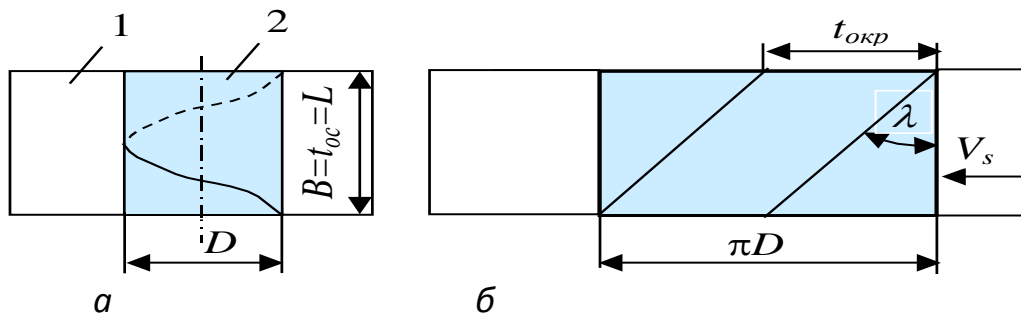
Резание фрезой с винтовой режущей кромкой:
